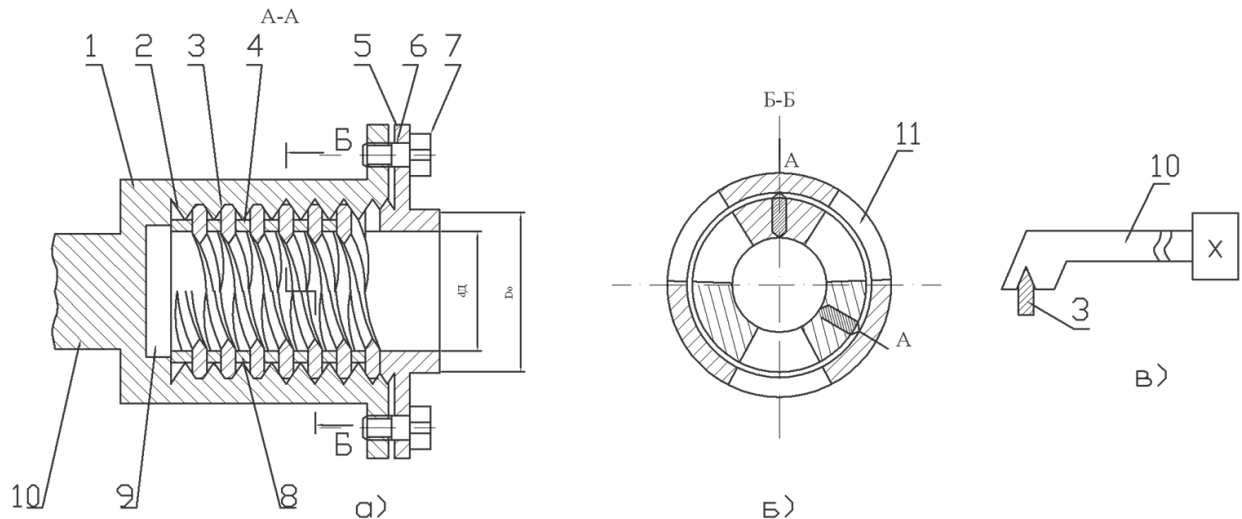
Технологічний пристрій для формування різьбового профілю в гнучких гвинтових заготовках.
